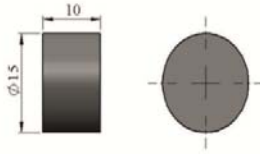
Alaşımların üretiminde kullanılan kokil kalıbın teknik resmi (Technical drawing of the mould used in casting of the alloys)
